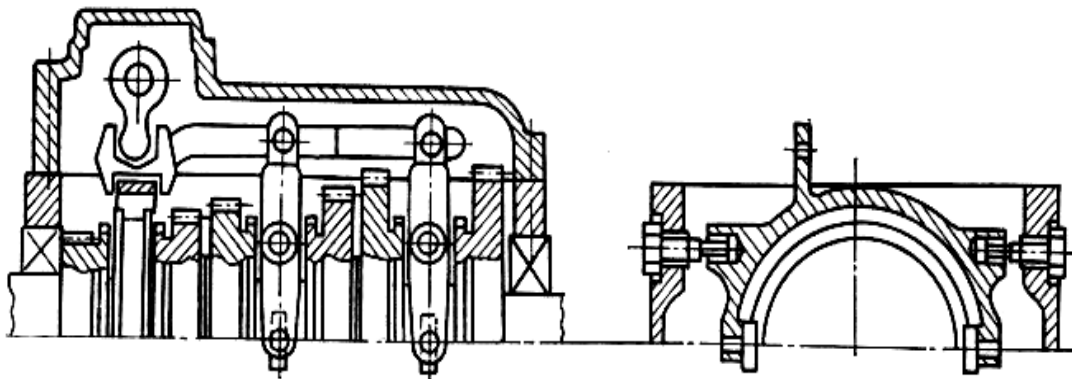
Конструкция механизма переключения передач с качательным движением вилок
